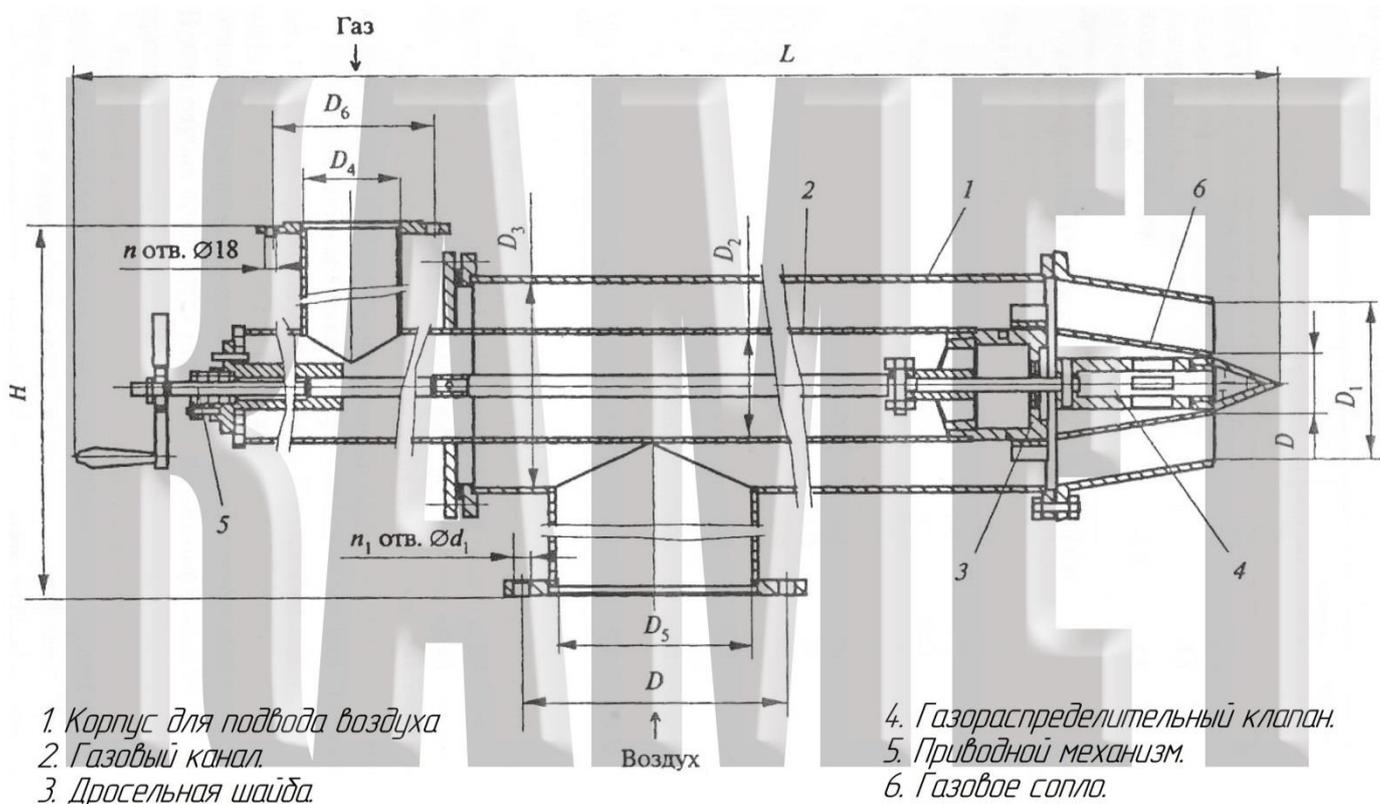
Схема горелки с основными габаритными и присоединительными размерами.
